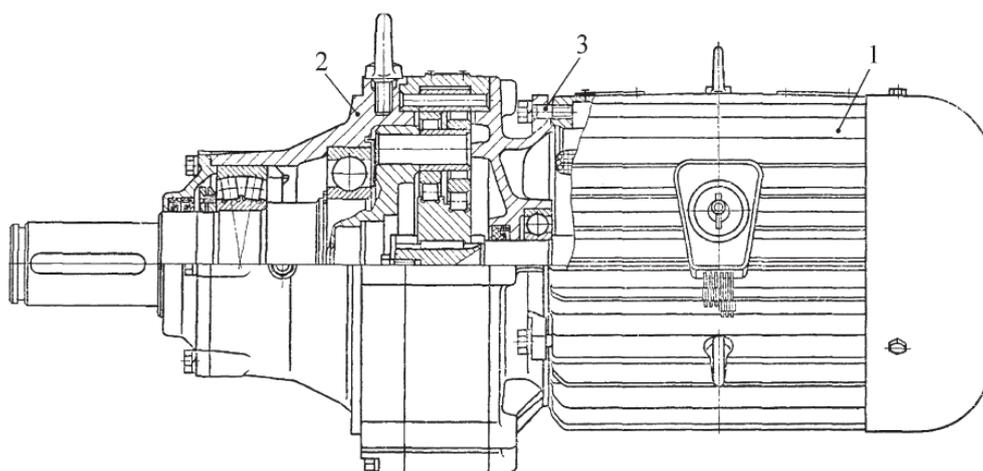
Планетарно-цевочный мотор-редуктор
